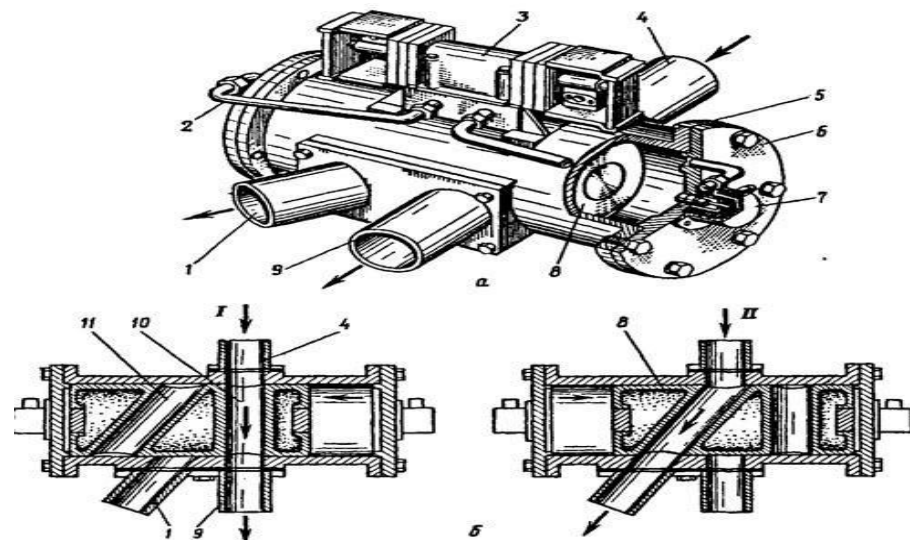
Двухпозиционный переключатель с пневмоприводом: а — общий вид; б — схема работы
